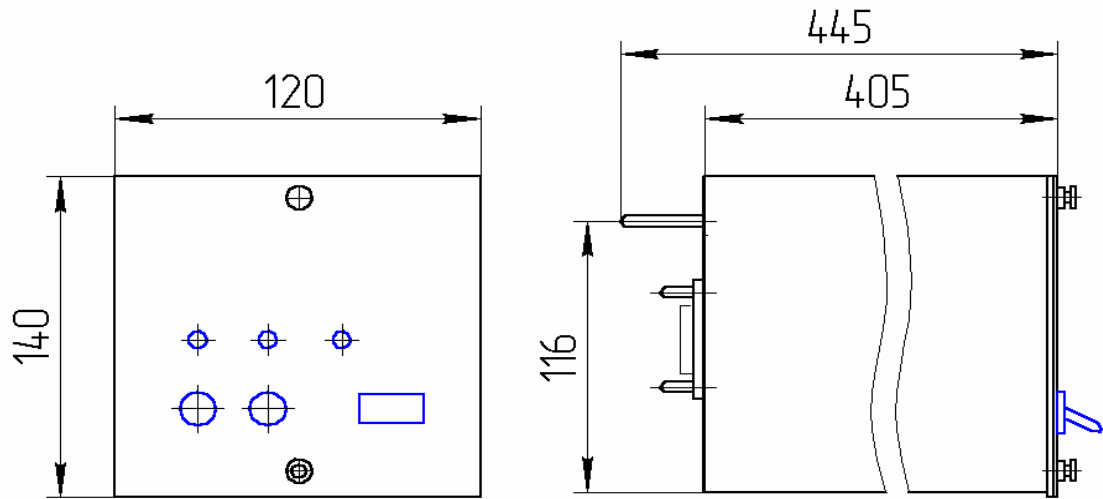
Габаритный чертеж БП в каркасе типа УТК1
